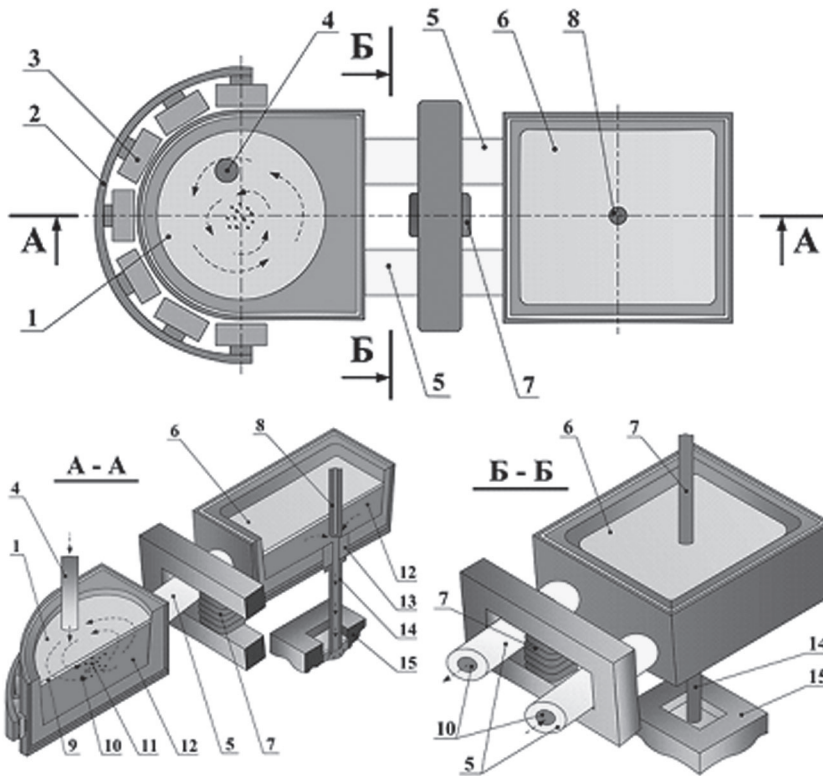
Двухкамерный промежуточный ковш с электромагнитным перемешивателем для создания вращающегося магнитного поля: 1 – приемная камера; 2 – удерживающее кольцо; 3 – электромагниты; 4 – защитная труба; 5 – каналы; 6 – рабочая камера; 7 – индуктор; 8 – стопор; 9 – теплоизолирующая смесь; 10 – потоки жидкой стали; 11 – неметаллические включения; 12 – жидкая сталь; 13 – стакан-дозатор; 14 – погружной стакан; 15 – кристаллизатор
